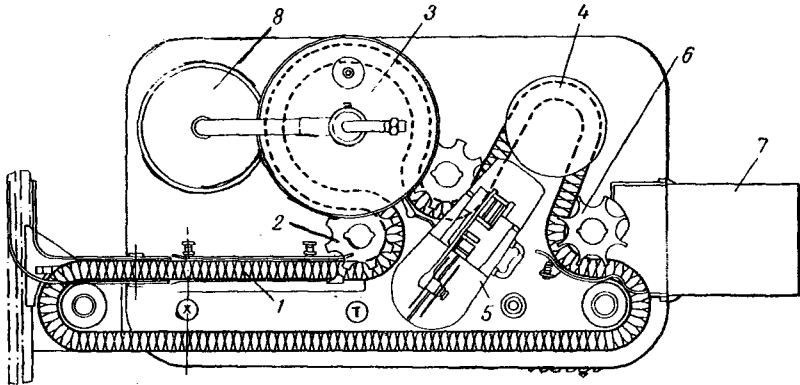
Схема разливно-укупорочного автомата «Юдек» (вид сверху):
